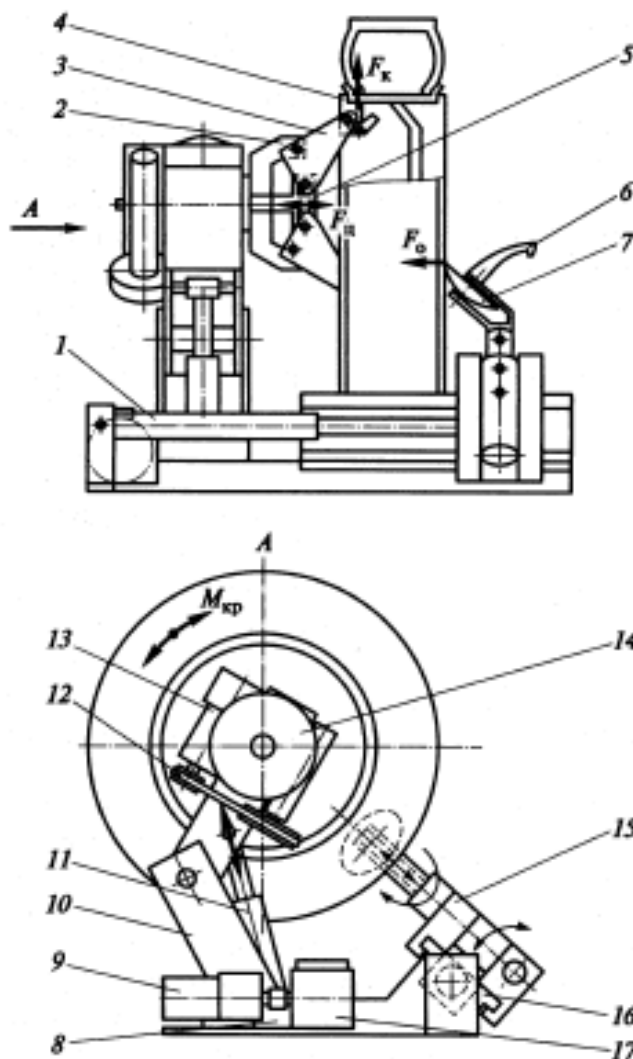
Схема стенда для монтажа и демонтажа шин колес грузовых автомобилей (стрелками на виде А показаны направления движения монтажной стойки и монтажной консоли):
